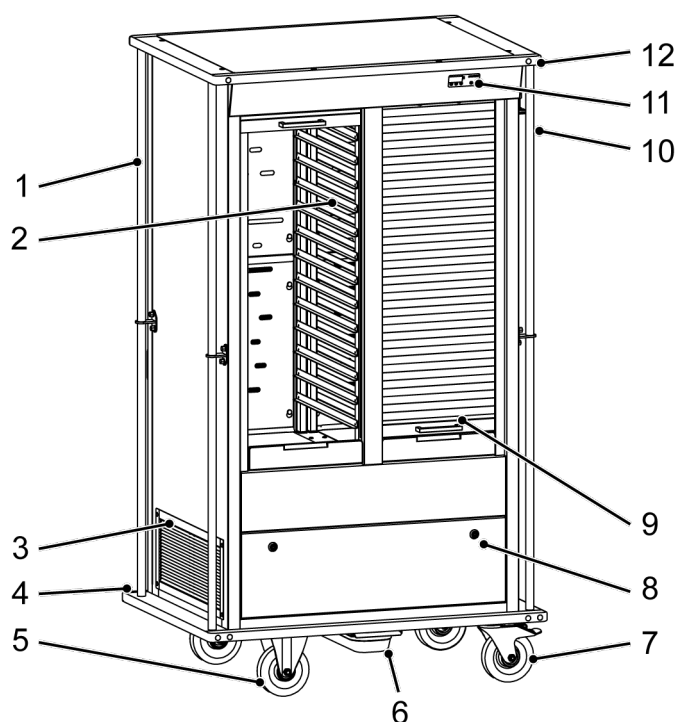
Vue d'ensemble de CoolMultiMobil
